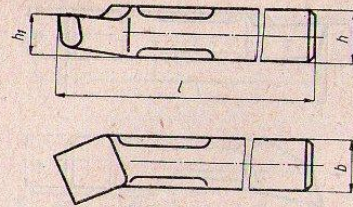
Soustružnické nože hladicí, ČSN 22 3532:
